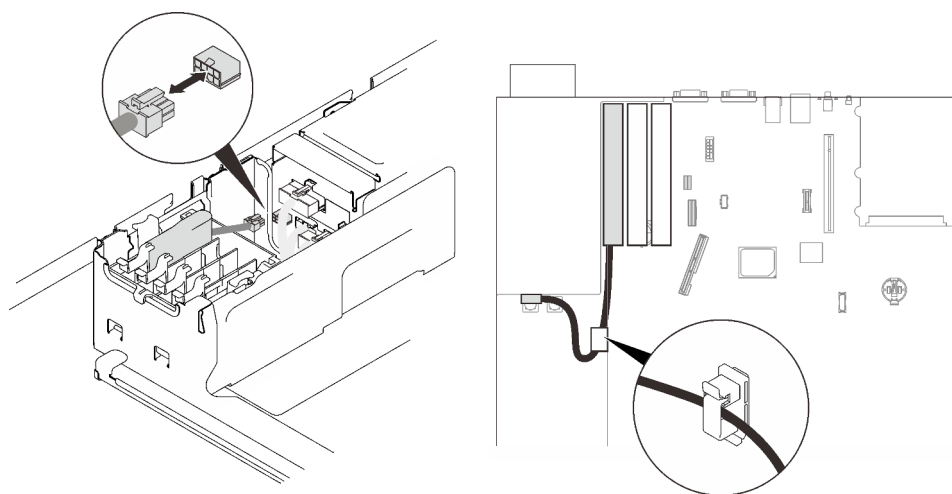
Scollegamento dei cavi del modulo di alimentazione flash
